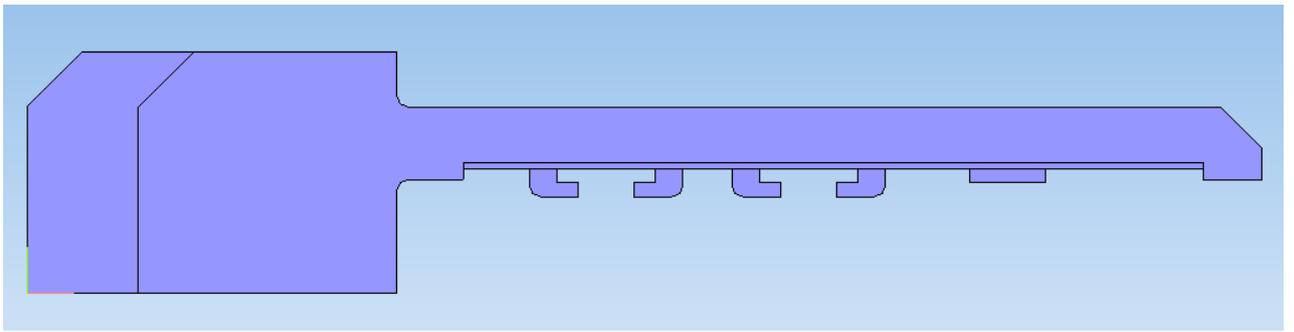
Трехмерная модель корпуса координатно-измерительной машины Moga Primus (вид сбоку)
